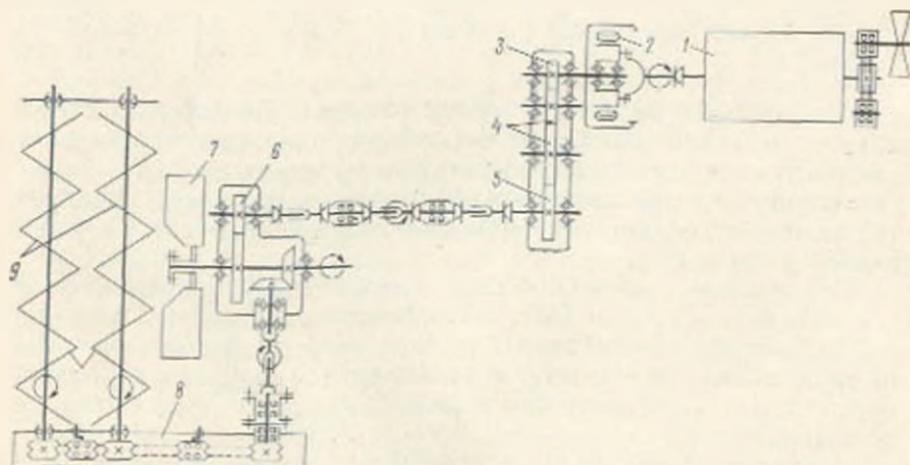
Кинематическая схема шнеко-роторного снегоочистителя СЭ-211: 1 — двигатель силовой установки 1Д12ВС; 2 — швно-пневматическая муфта; 3 — ведущая шестерня промежуточного редуктора; 4 — промежуточная шестерня; 5 — ведомая шестерня промежуточного редуктора; 6 — редуктор привода ротора; 7 — ротор; 8 — цепной редуктор привода шнека; 9 — шестерни
